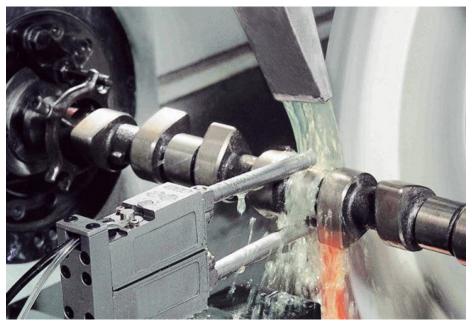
Пример обработки на станке с ЧПУ, содержащий сервопривод
